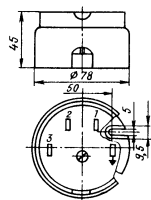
Габаритные, установочные размеры розетки круглой формы для открытой установки
